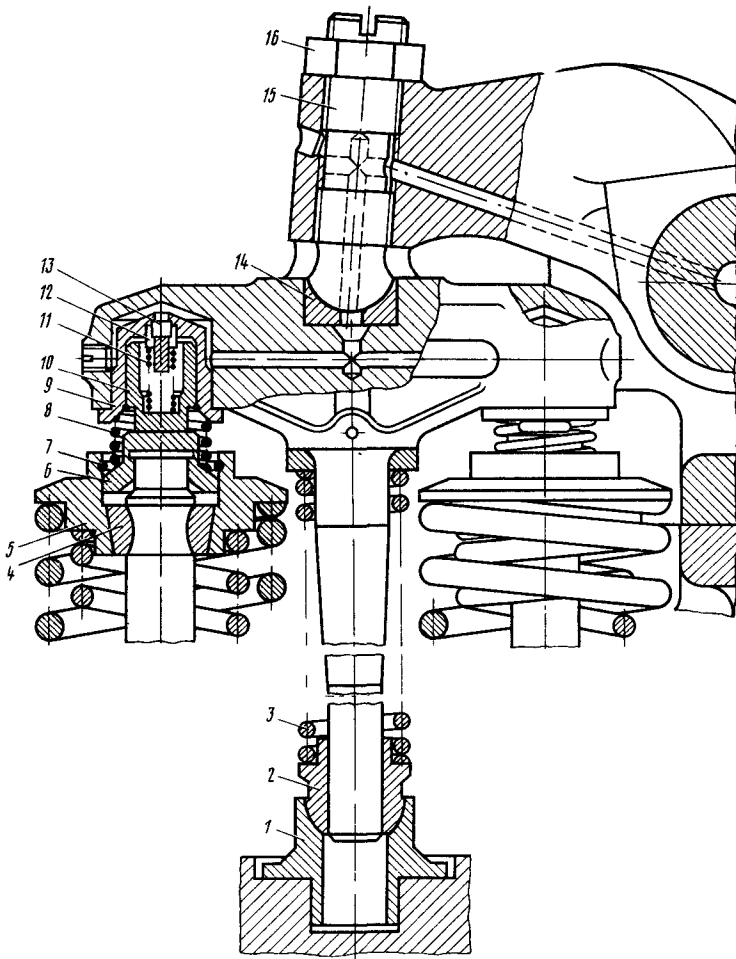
Привод клапанов крышки цилиндров дизеля 11Д45
